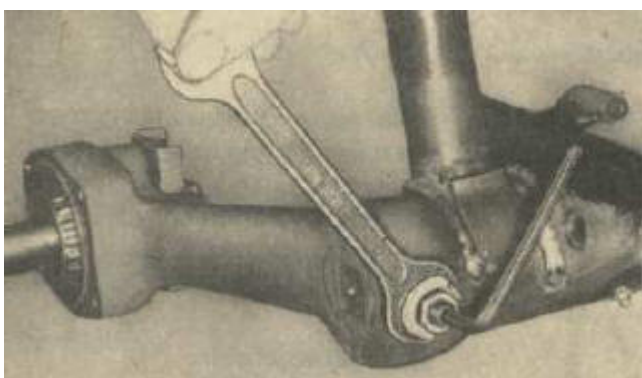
Lösen des M-12-Gewindestiftes durch Festhalten des Stiftes mit einem Innensechskantschlüssel und Aufdrehen der M-12-Mutter mit einem Gabelschlüssel SW 19
